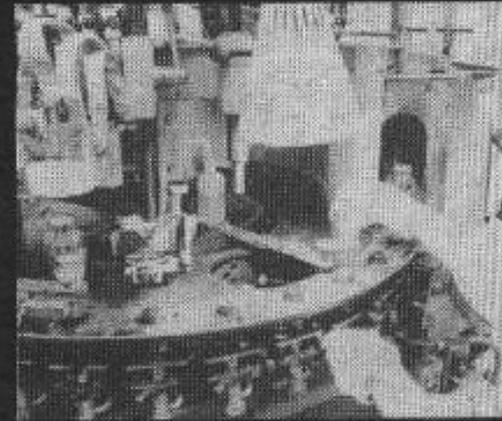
Soudure du bulbe sur l'embase en verre.
